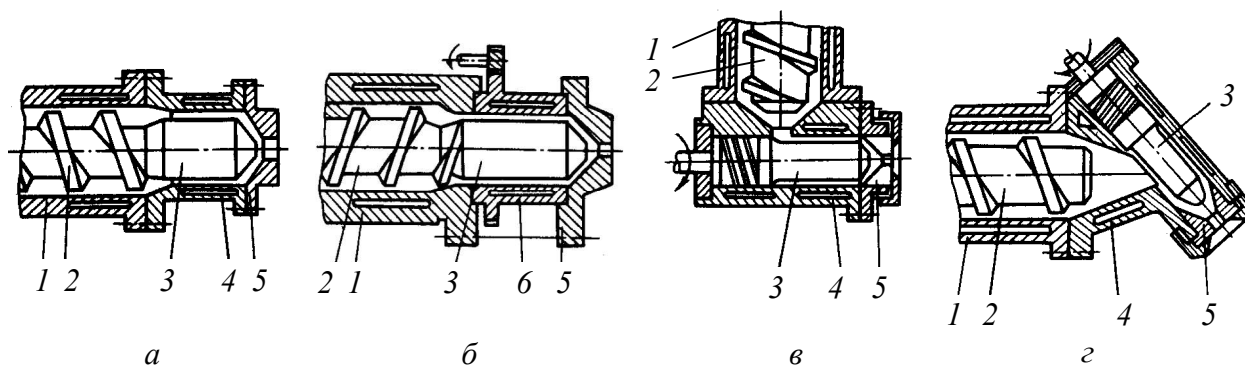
Схеми змішувальних елементів без регулювання (а) і з регулюванням (б–г) відносної швидкості обертання їхніх робочих поверхонь [52]: 1 – циліндр; 2 – черв’як; 3 – дорн; 4 – корпус головки; 5 – формувальний інструмент; 6 – обертова втулка
